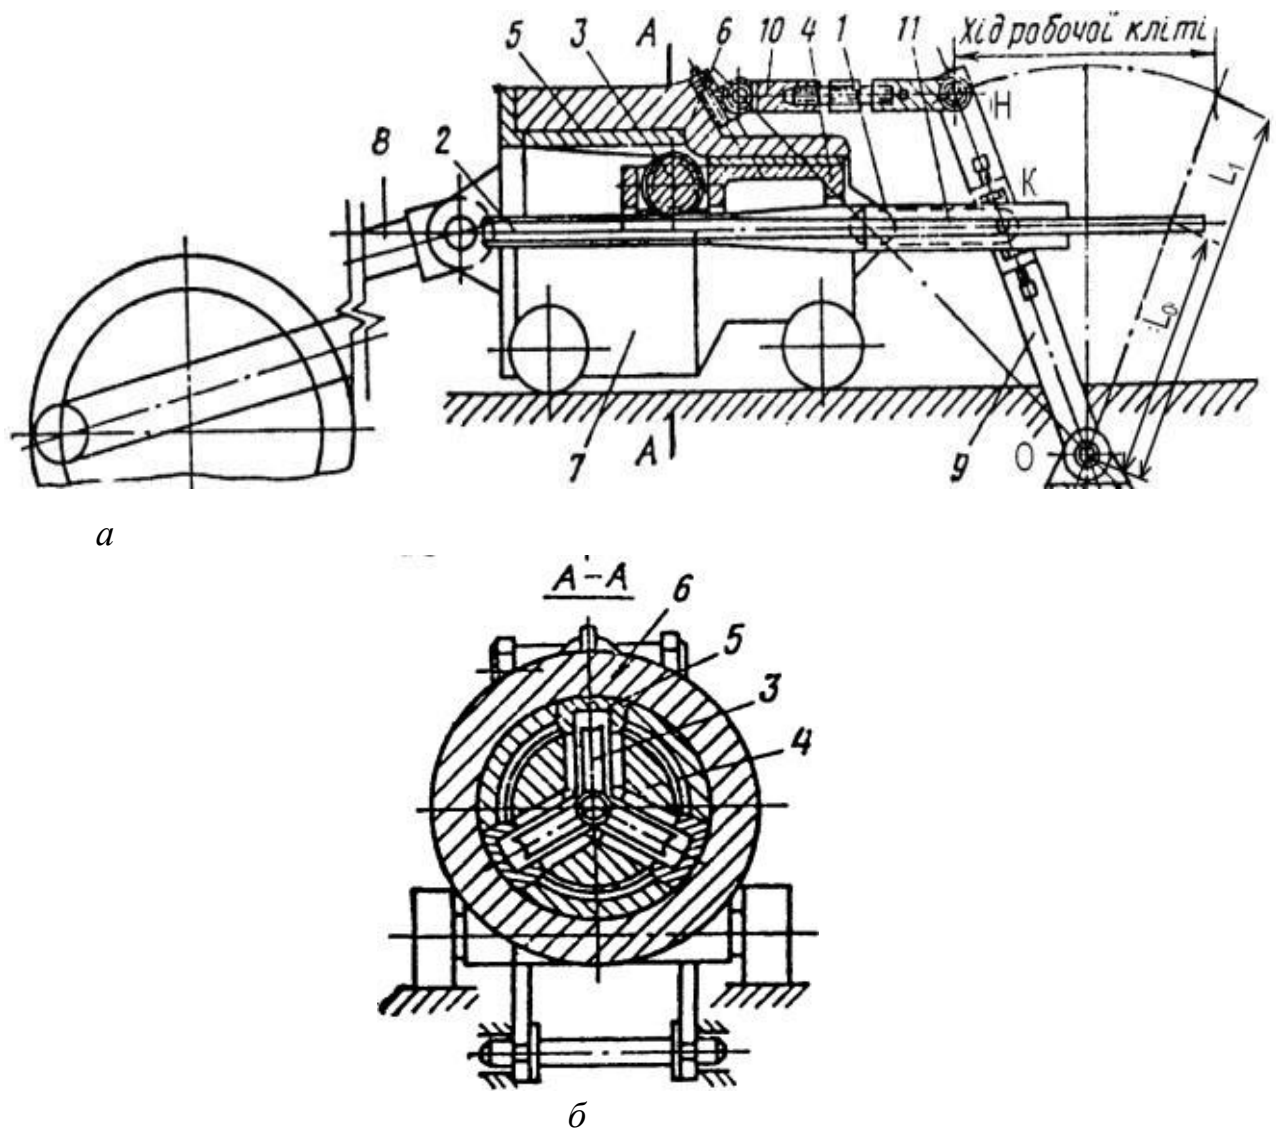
Робоча кліть стану ХПТР: поздовжній розріз (а), поперечний переріз (б): 1 – труба; 2 – циліндрична оправка; 3 – ролики; 4 – сепаратор; 5 – планки; 6 – втулка каретки; 7 – візок; 8 – кривошипно-шатунний механізм; 9 – важіль
